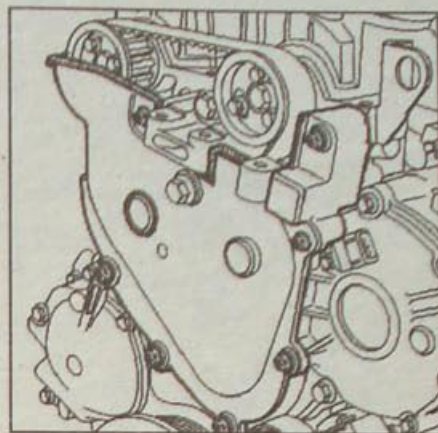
Расположение нижнего кожуха привода газораспределительного механизма
